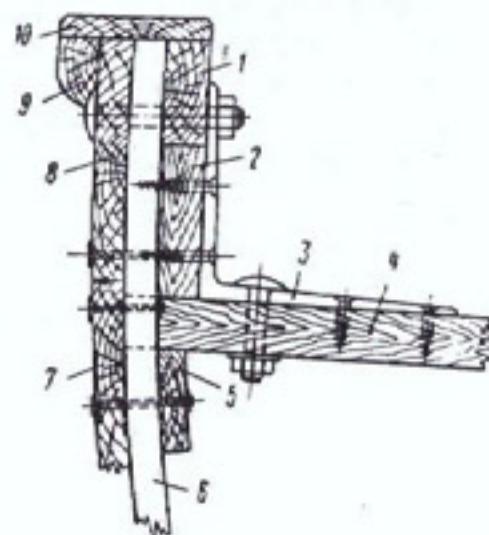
Планшир, буртик и крепление банки на открытой рабочей шлюпке.
